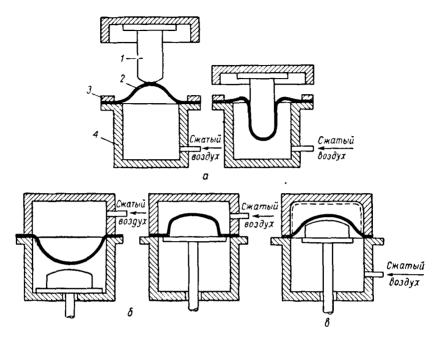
Схемы использования способа поддува для получения изделий большой глубины с равномерными стенками:
